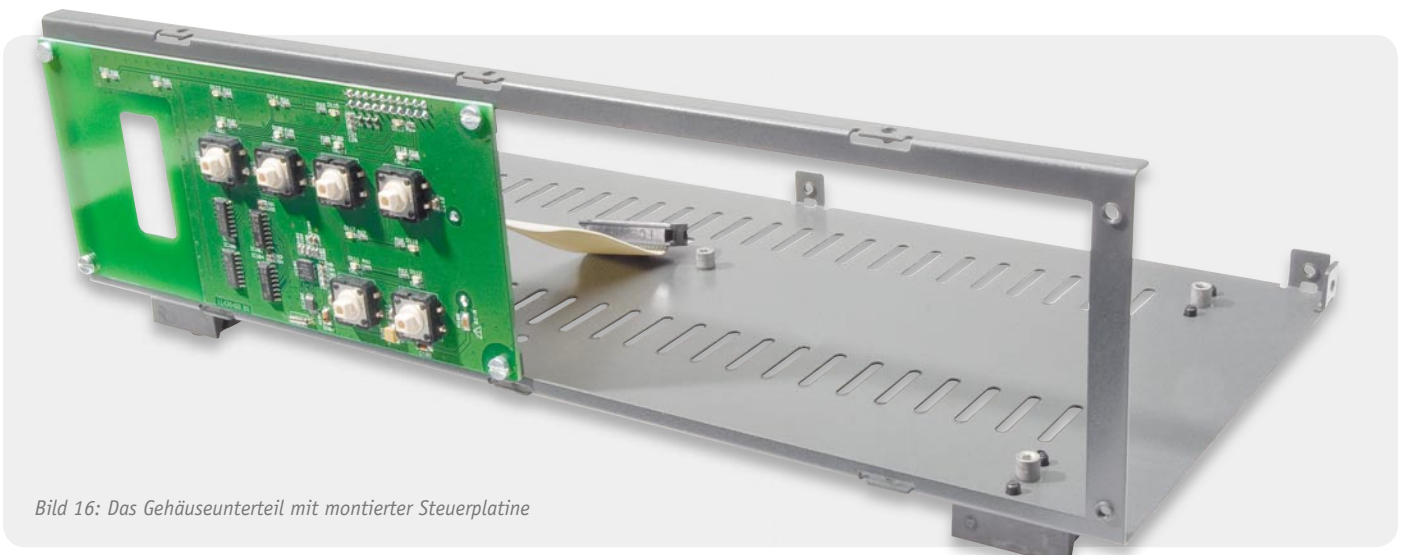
Das Gehäuseunterteil mit montierter Steuerplatine
